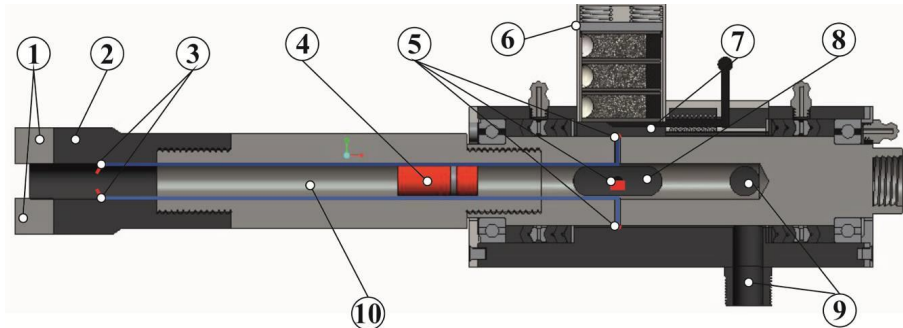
Конструкція механізму для вибухо-механічного руйнування гірських порід: 1 – різці; 2 – ріжучий інструмент комбінованої дії; 3 – пластини контактні; 4 – заряд вибухової речовини; 5 – напайки контактні; 6 – касета з зарядами вибухової речовини; 7 – затвор; 8 – отвір для подачі зарядів вибухової речовини до продувного каналу; 9 – отвори для нагнітання стисненого повітря; 10 – продувний канал
